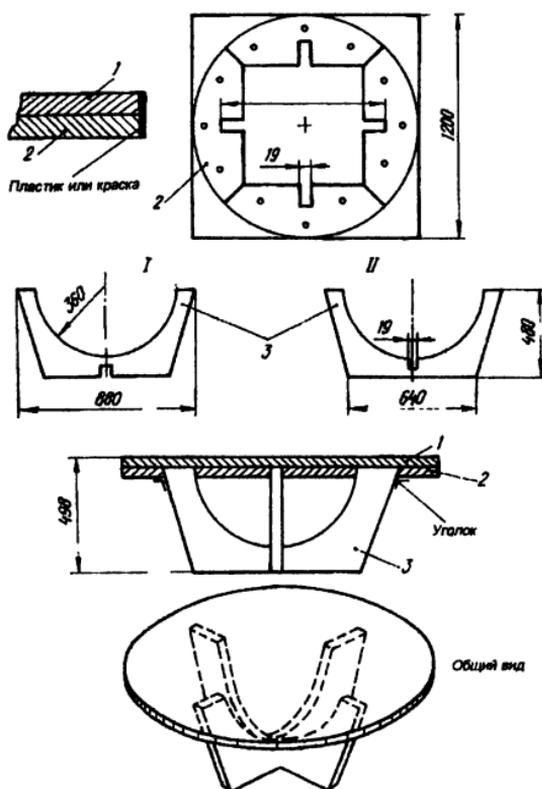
Круглый журнальный столик: общий вид и сборочный чертеж
